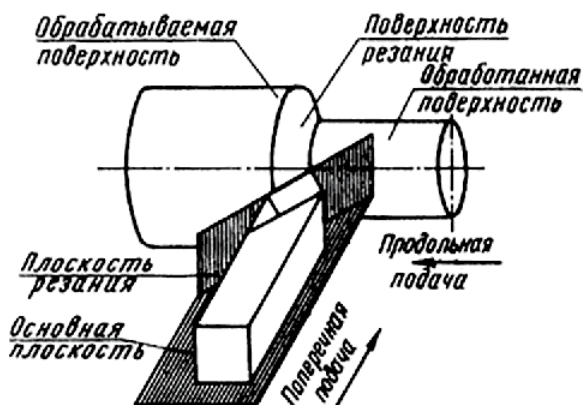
Основные поверхности заготовки и условные плоскости для изучения геометрии резца
